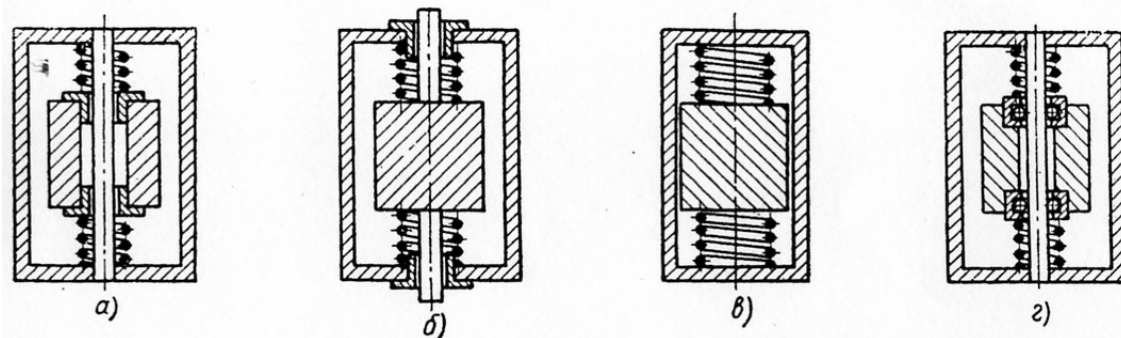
Конструкции пружинного подвеса с дополнительными направляющими элементами
